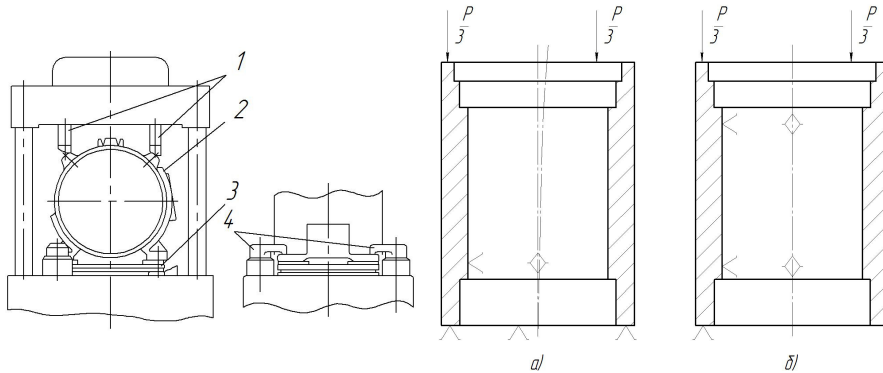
Схема закріплення станини двигуна типу АО2-7 на автоматичній лінії мод. 1Л110. Позначено: 1 – верхні притискачі; 2 – оброблювана станина; 3 – супутник; 4 – гідропритискачі.
